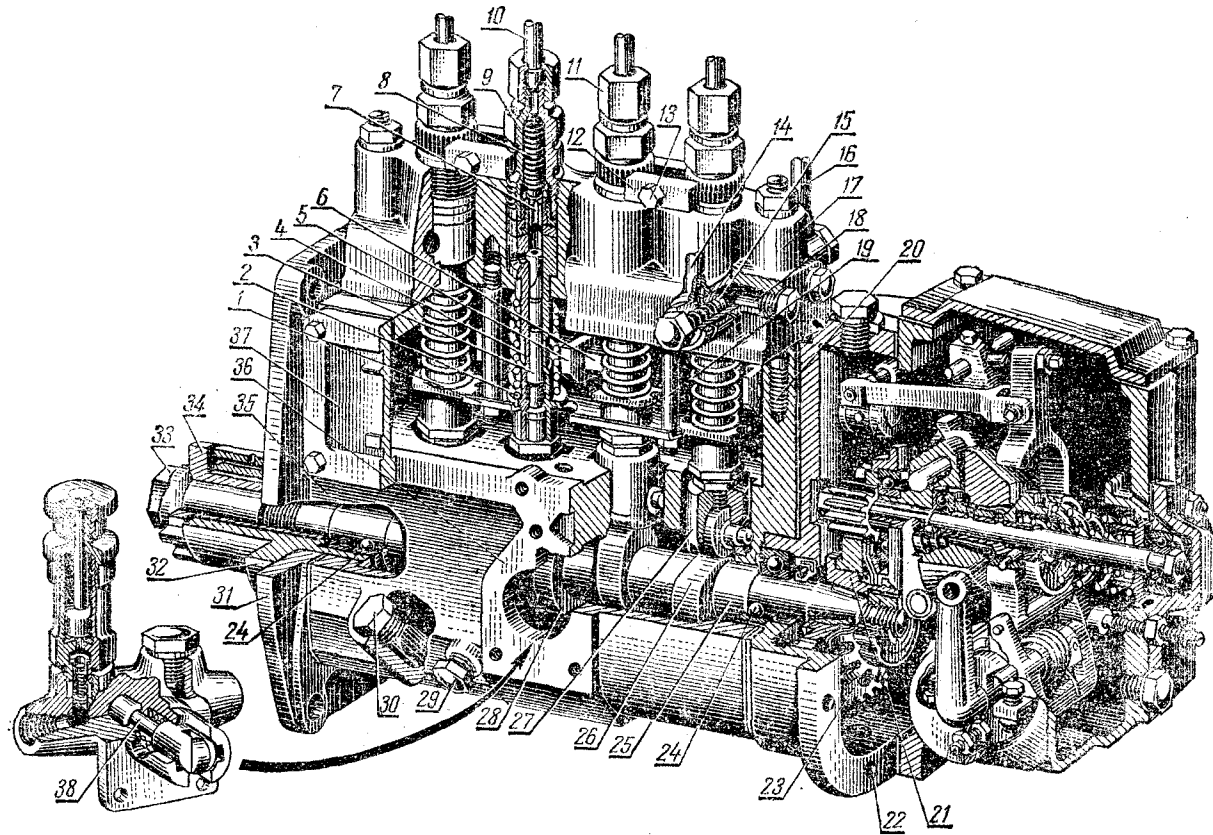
Топливный насос типа ЛСТН-48510 с регулятором:
